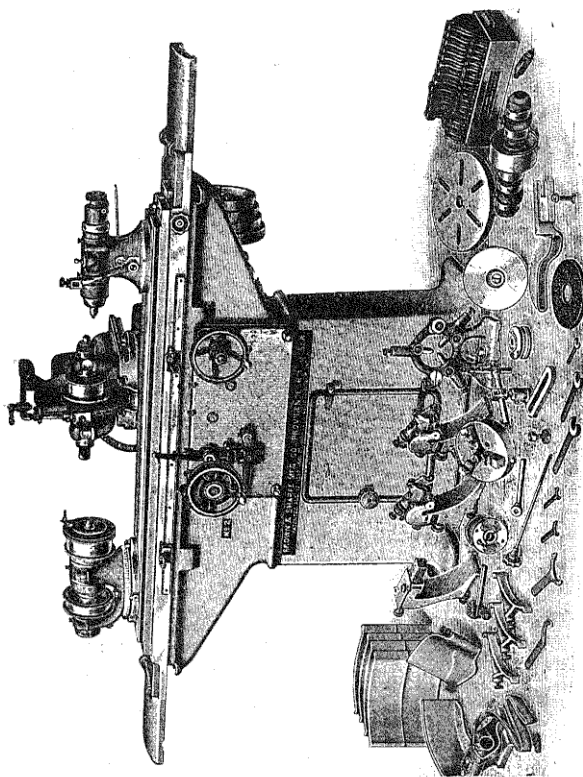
Machine à rectifier universelle Brown et Sharpe.
